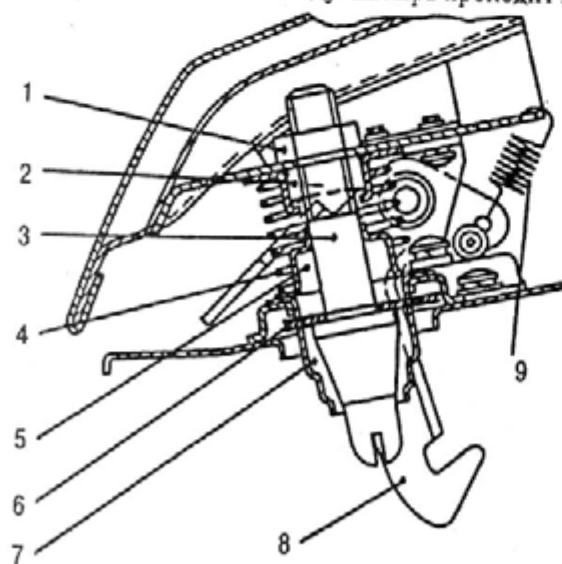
Замок капота и предохранительный крючок: 1 - контргайка; 2 - гайка неподвижная с гайкодержателем; 3 - штырь; 4 - пружина штыря; 5 - фланец пружины; 6 - щеколда; 7 - направляющая штыря; 8 - предохранительный крючок.
